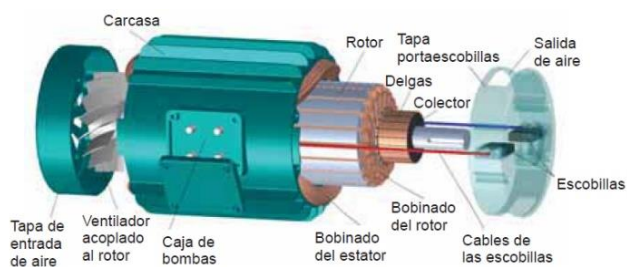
Perspectiva explosión de un pequeño motor de CD [33]
